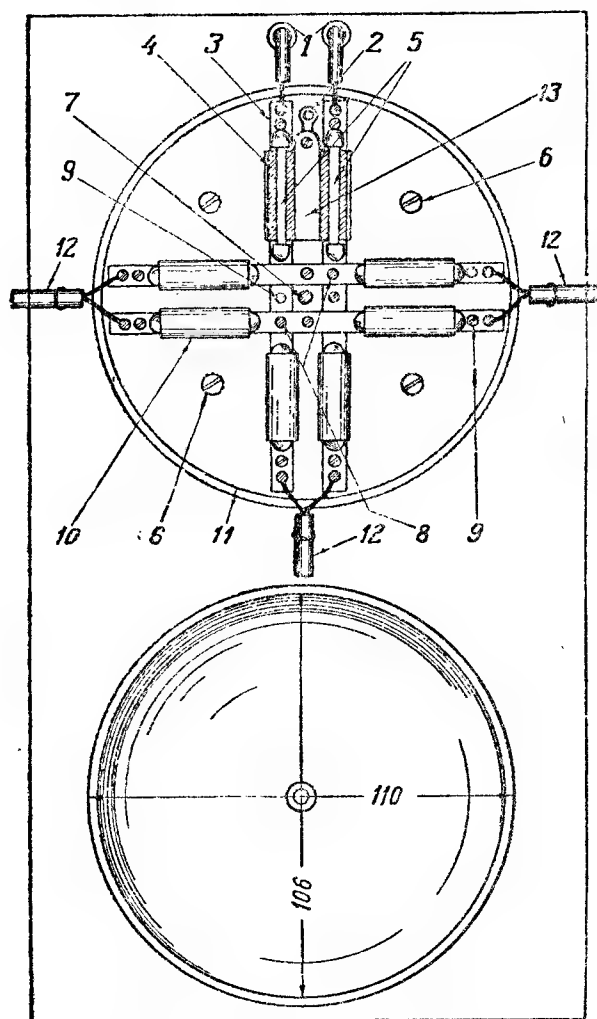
Устройство коробки: 1—вводные втулки; 2—отверстие для заземления; 3—металлические пластинки для крепления проводов; 4—угольные пластинки; 5—предохранители; 6—шурупы, крепящие коробку к стене; 7—болт для крепления крышки коробки; 8—болты, крепящие шины коробки; 9—болты, крепящие шины к основанию коробки; 10—емкостные ограничители; 11—вырез для краев крышки коробки; 12—ответвления к абонентам; 13—металлическая пластинка для заземления
